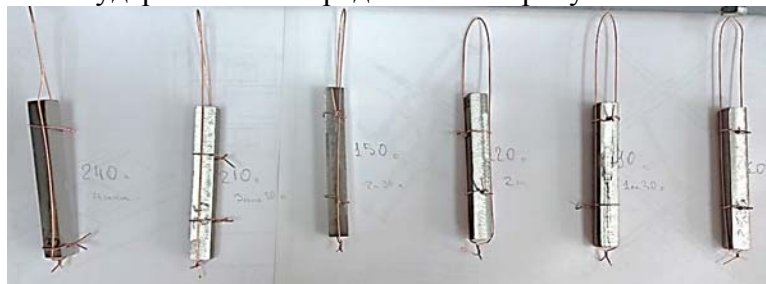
Сварные темплеты, подготовленные к проведению термической обработки
